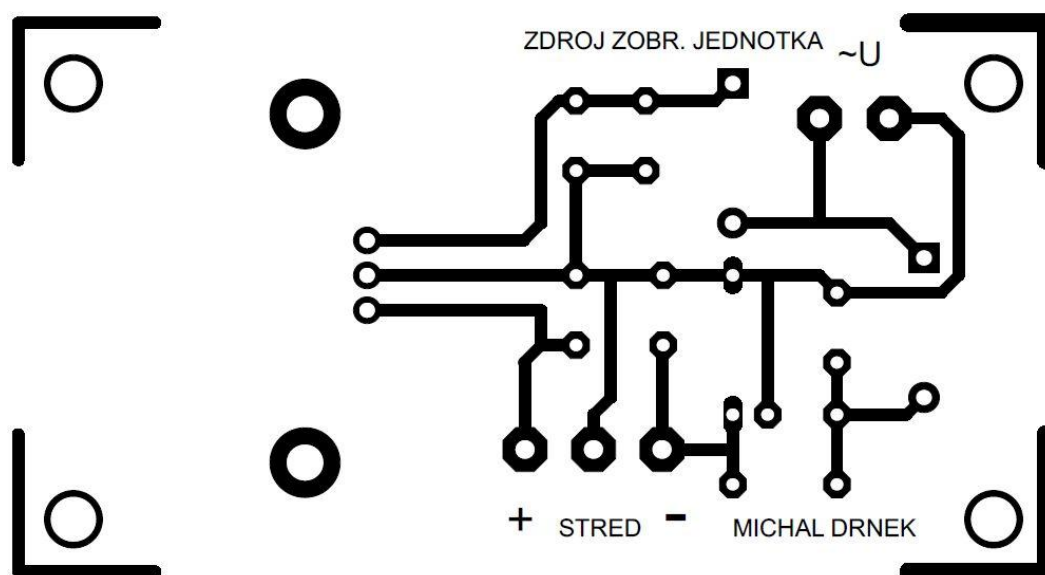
Schéma zapojení zdroje ventilátoru
